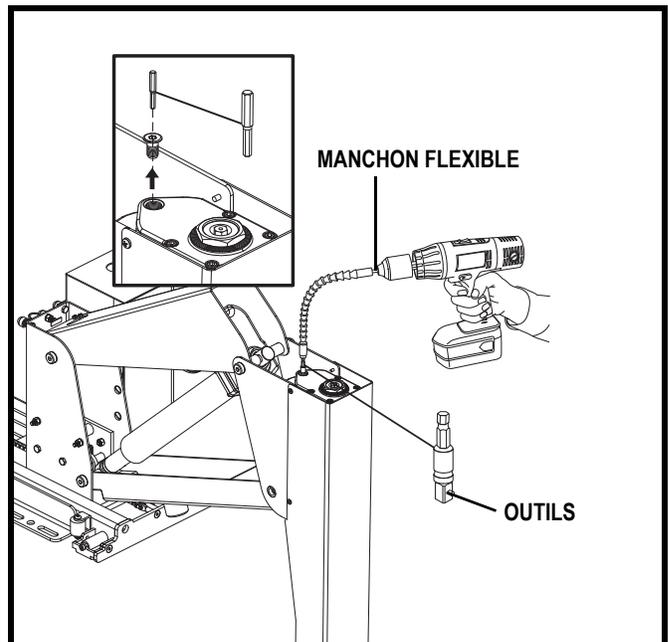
A. Élever ou abaisser la plateforme - Retirez la vis pour exposer l'orifice de réglage (Backpacker MV SEULEMENT)
